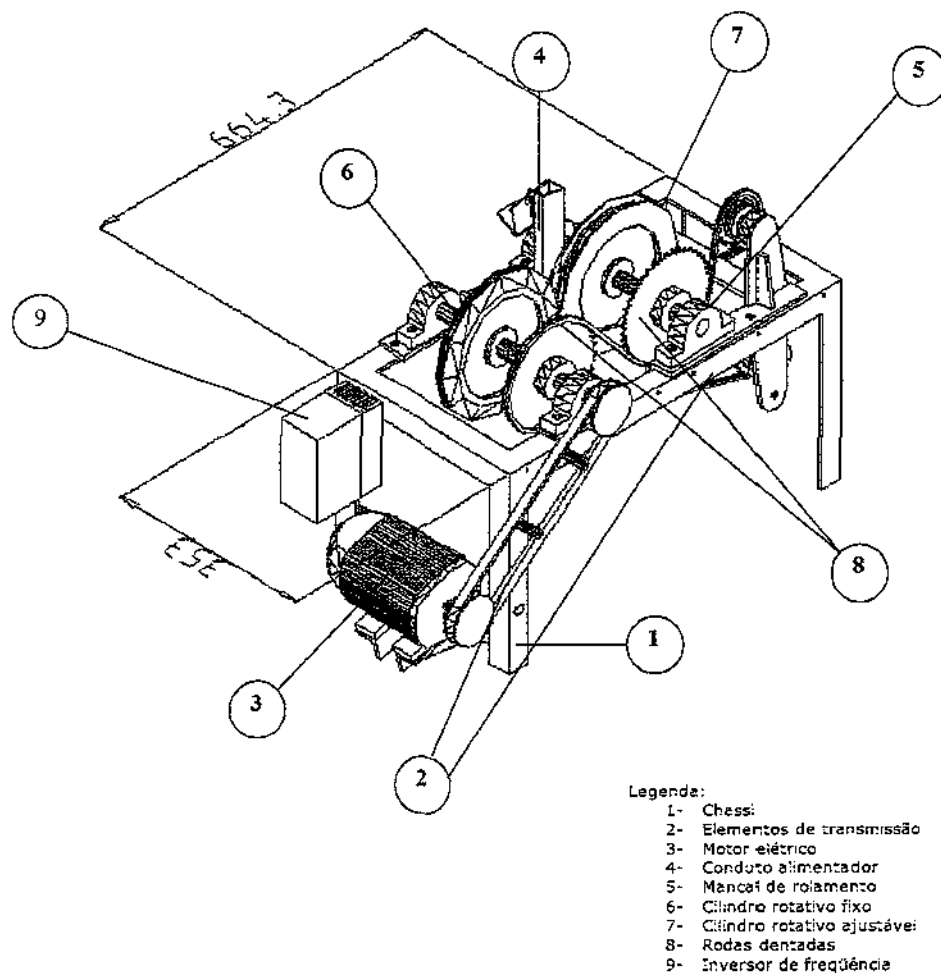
Vista do protótipo decortificador de castanha de caju com mecanismo cilíndrico rotativo mostrando seus principais componentes.
